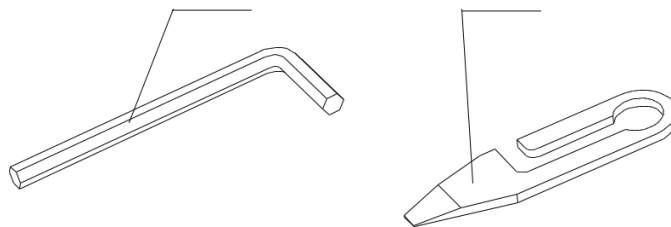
Gesamtansicht der Schraubenschlüssel
